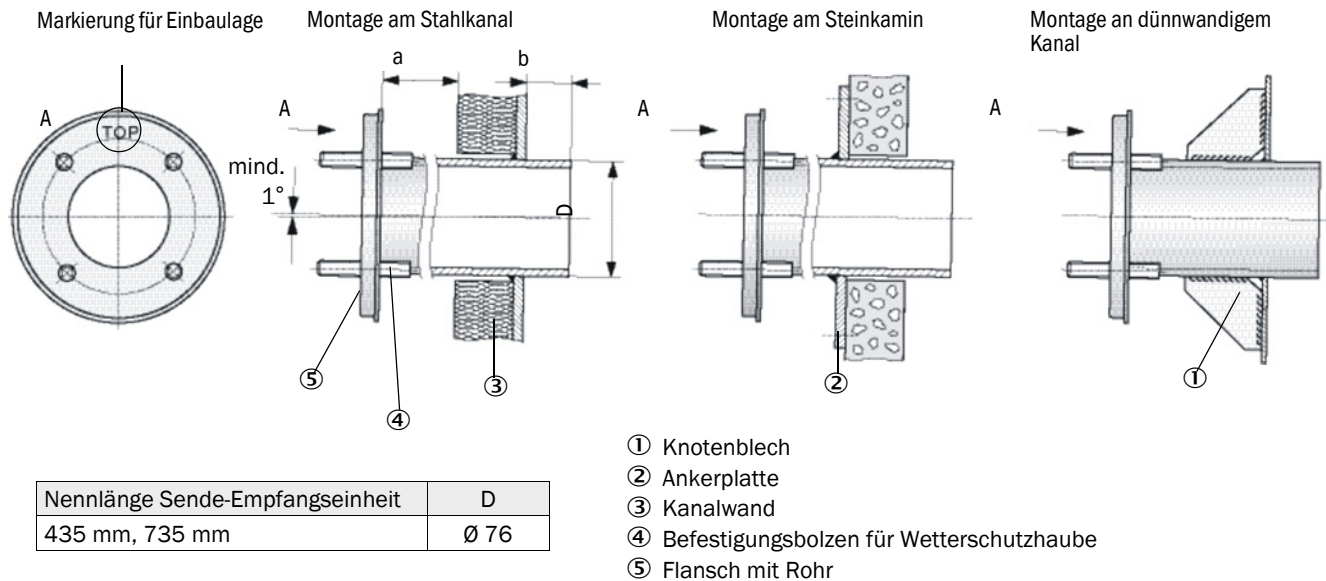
Einbau des Flansches mit Rohr (Darstellung für Standardausführung)
